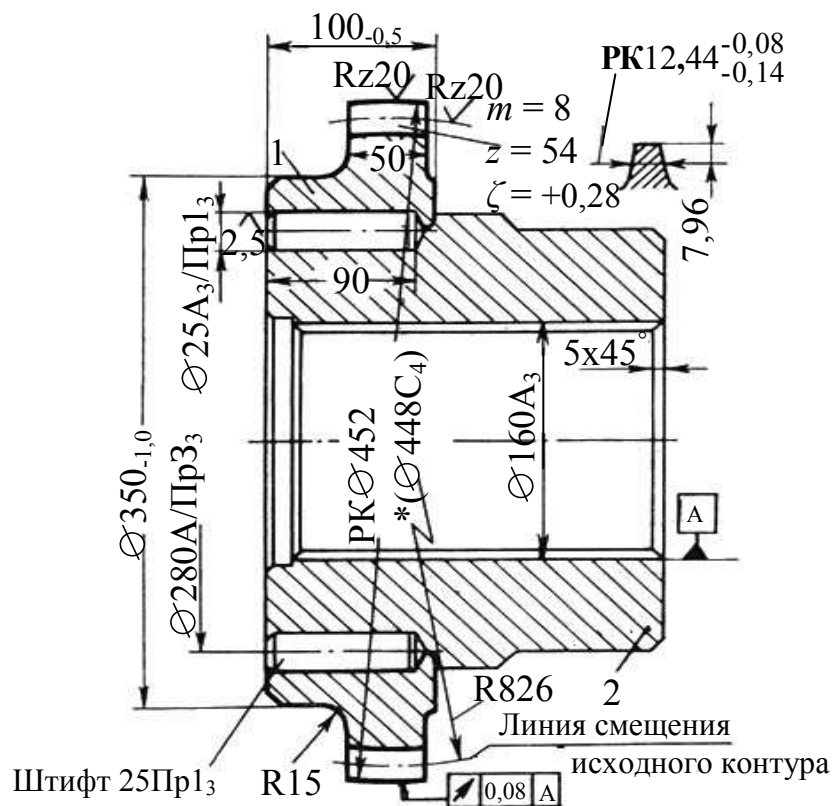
Ремонтный чертеж восстановления венца втулки зубчатой муфты: 1 – исходная деталь; 2 – бандаж ремонтного корригирования; * – размер исходный по чертежу
